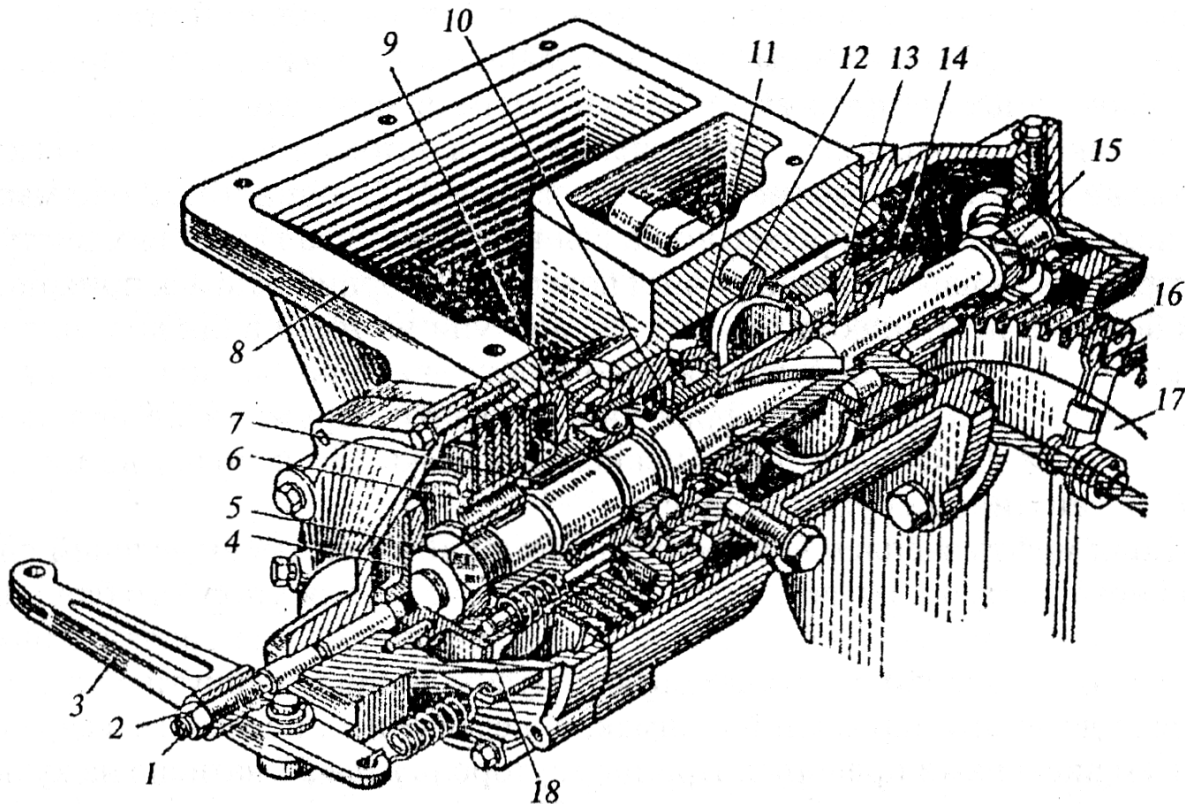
Механізм передачі (редуктор) пускового двигуна ПД-8м:
